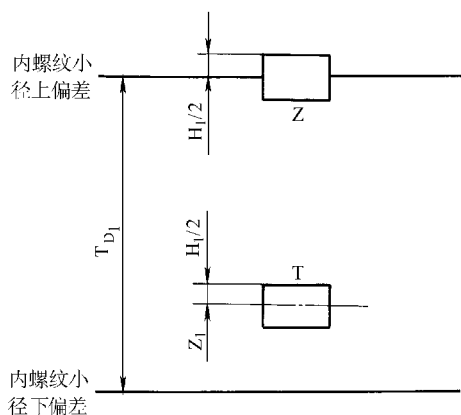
检验工件内螺纹小径用的光滑极限量规尺寸公差带图
